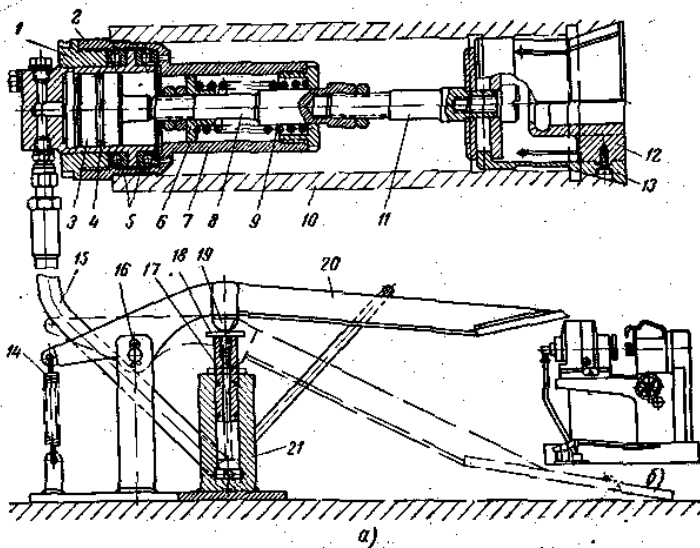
Пружинный зажим с механо-гидравлическим управлением: а — общий вид, б — монтаж приспособления на станке
